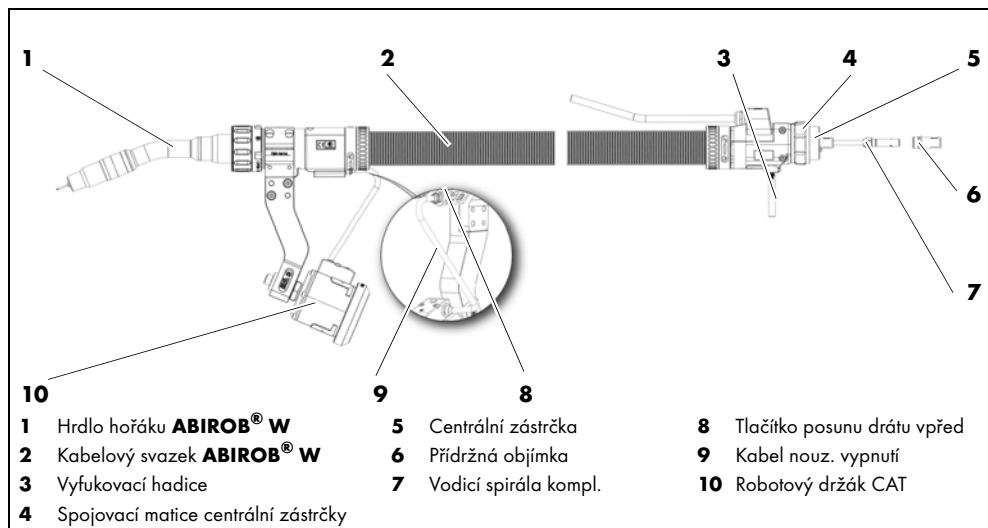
Montáž hrdla hořáku ABIROB® W
